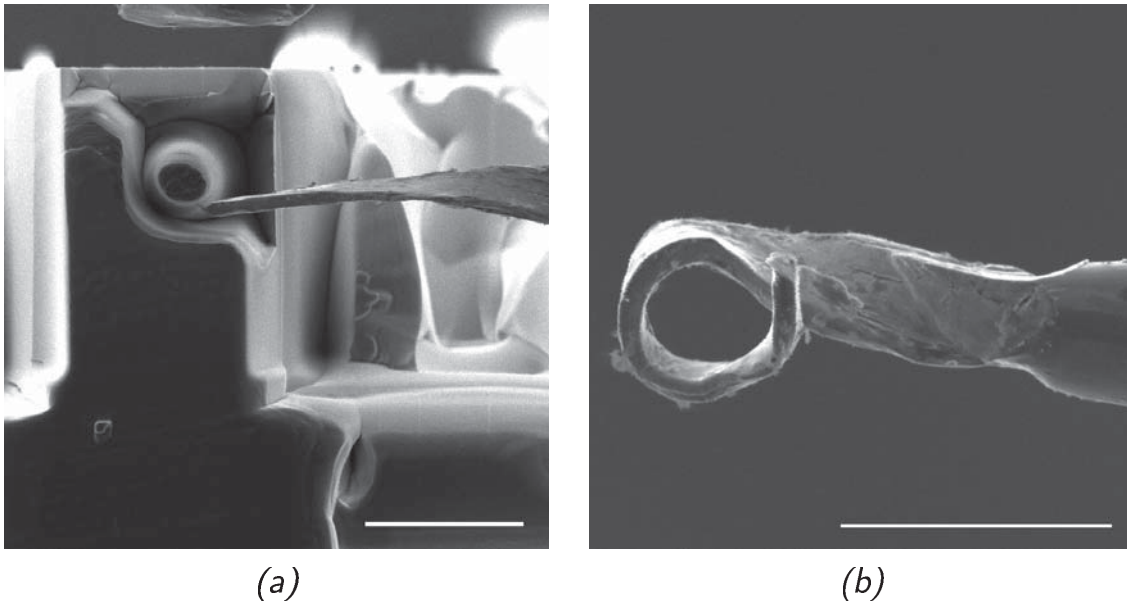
Si-Werkzeug für das Rollbiegen mit zylindrischem rückfederndem Biegearm auf Bild (a). Bild (b) zeigt eine mit dem Rollbiegewerkzeug gefertigte Windung aus einem flachgeformten Wolframhalbzeug (um 180° gedreht). (Maßstab: $5\ \mu\text{m}$)
